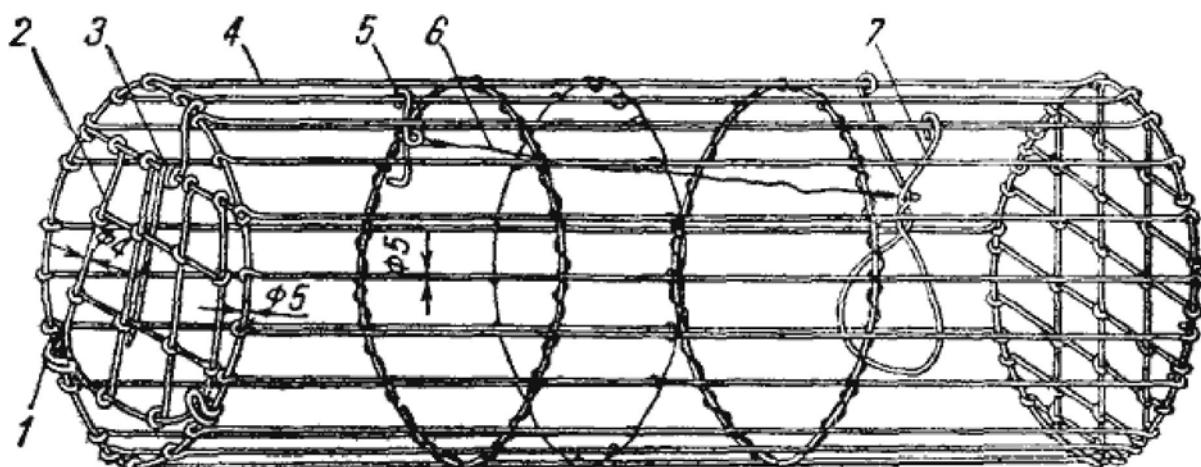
Белорусская живоловушка на бобра: 1 — упор дверцы; 2 — дверца; 3 — пружина дверцы; 4 — корпус; 5 — сторожок; 6 — тросик; 7 — насторожка; (φ — диаметр проволоки в мм)
